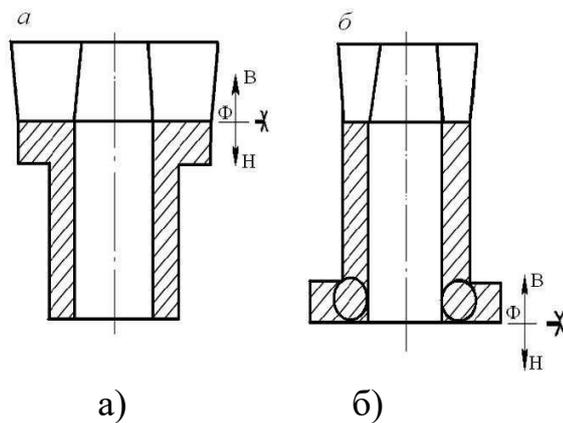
Положение в форме отливки «Корпус люка» [3, с. 70]:
